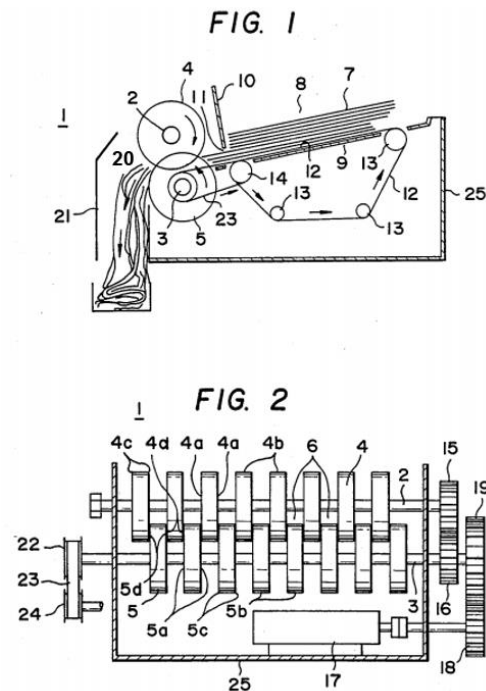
Shredding machine de papel com tabela dos componentes discriminados. (Adaptado de [19])
